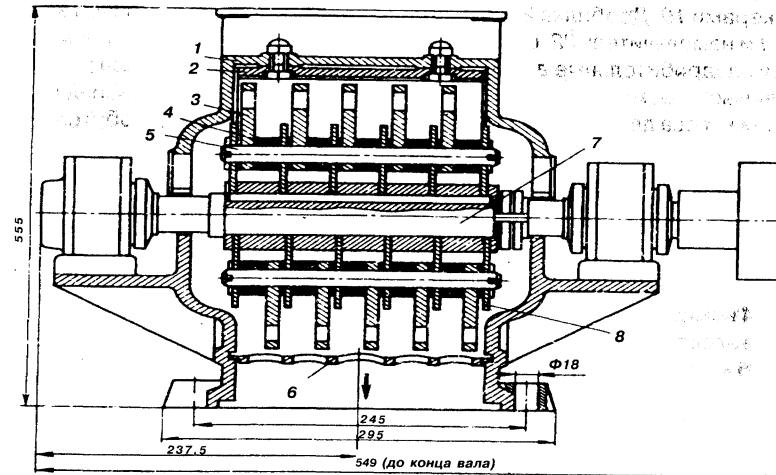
Общий вид дробилки К7-ФКЕ-10:
